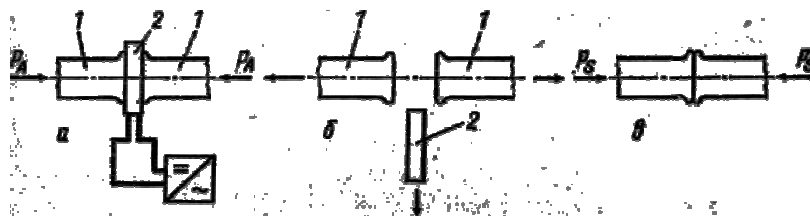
Принцип сварки нагретым инструментом: а — подогрев свариваемых деталей; б — отвод нагретого инструмента; в — стыкование (сварка); 1 — свариваемые изделия; 2 — нагретый инструмент; 3 — источник питания.
